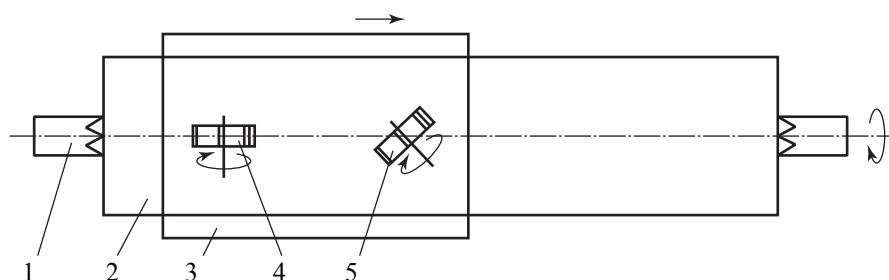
Принципиальная схема оцилиндровочного станка позиционно-проходного типа: 1 – вращающиеся зажимы; 2 – бревно; 3 – суппорт; 4 и 5 – цилиндрические фрезы
